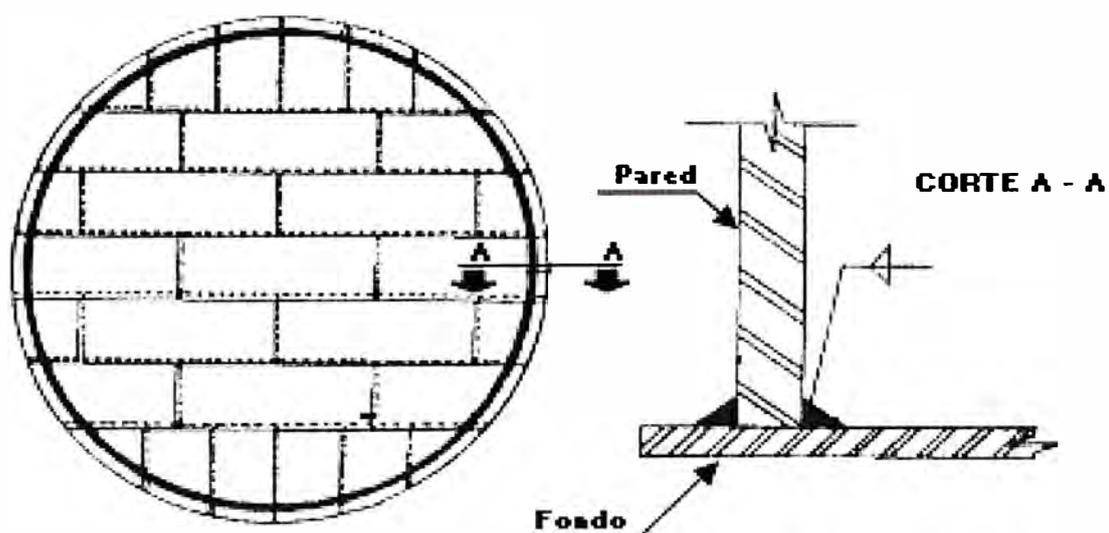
Arreglo típico de la distribución de las planchas del fondo
